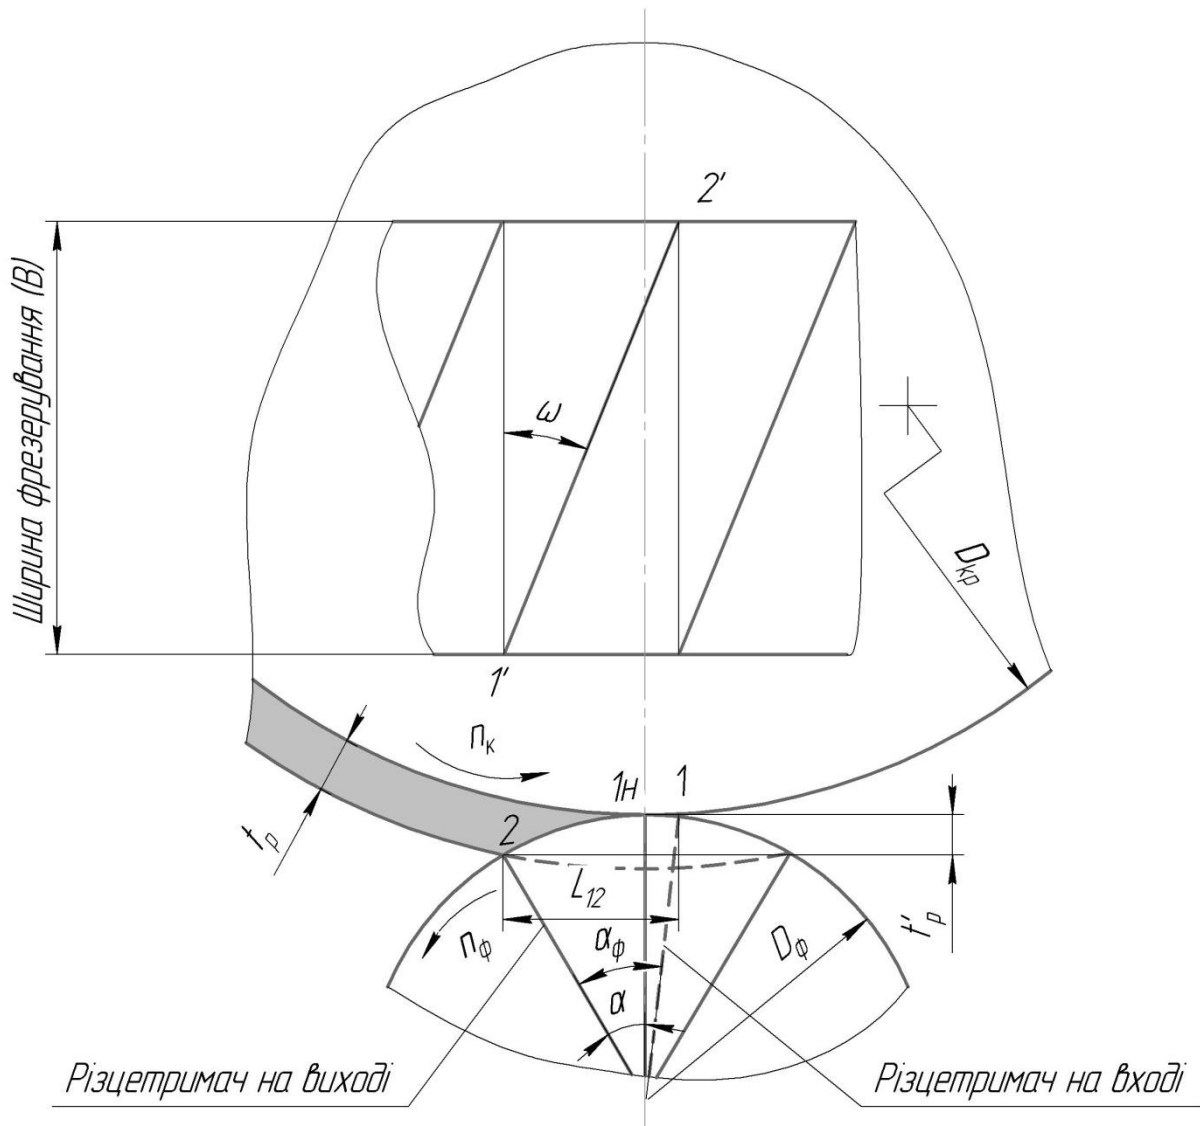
Схема умови рівномірного фрезерування колісної пари
